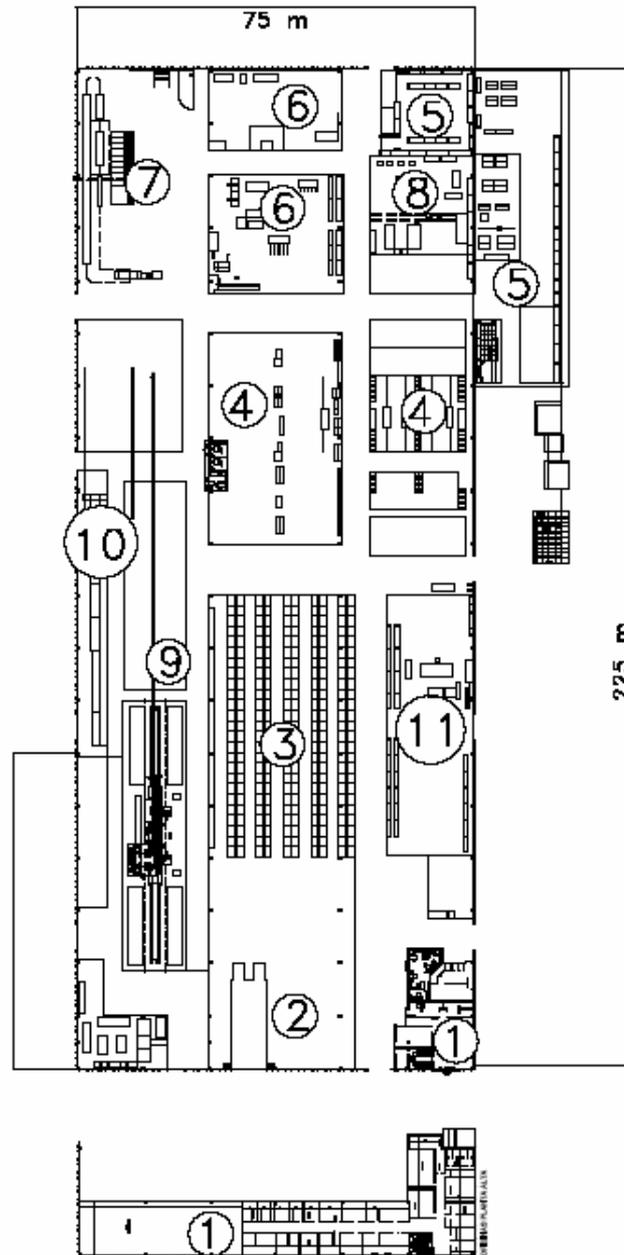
Lay out de la planta de Arneg S.A. en la ciudad de Rosario.
